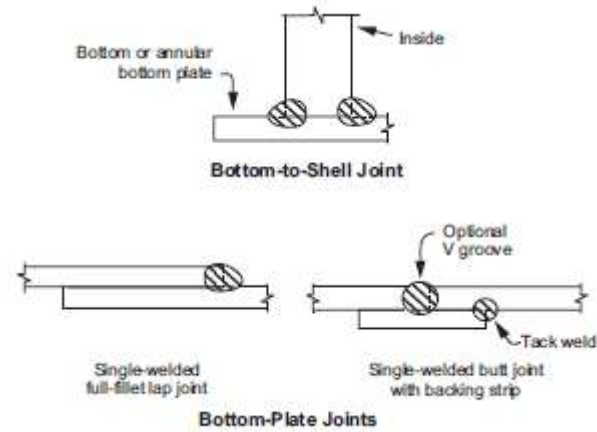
Soldaduras para juntas horizontales, F5.2 API 650.
